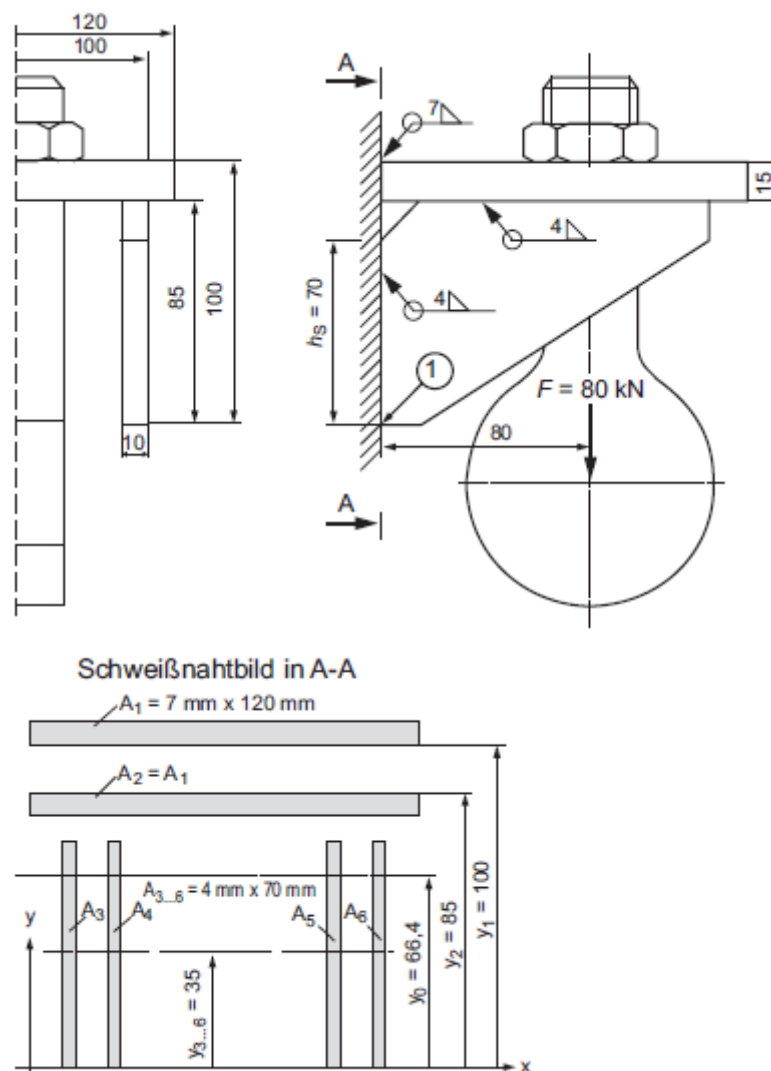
Geschweißte Konsole mit Seilspanner
